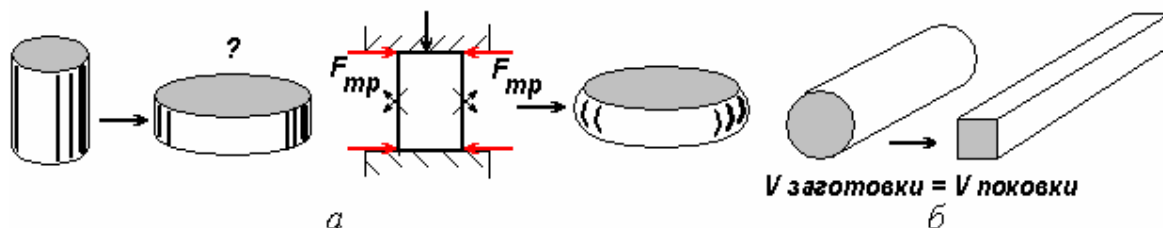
Бочкообразная форма поковки объясняется действием сил трения между заготовкой и бойками молота (а); объёмы поковки и заготовки равны (б)
